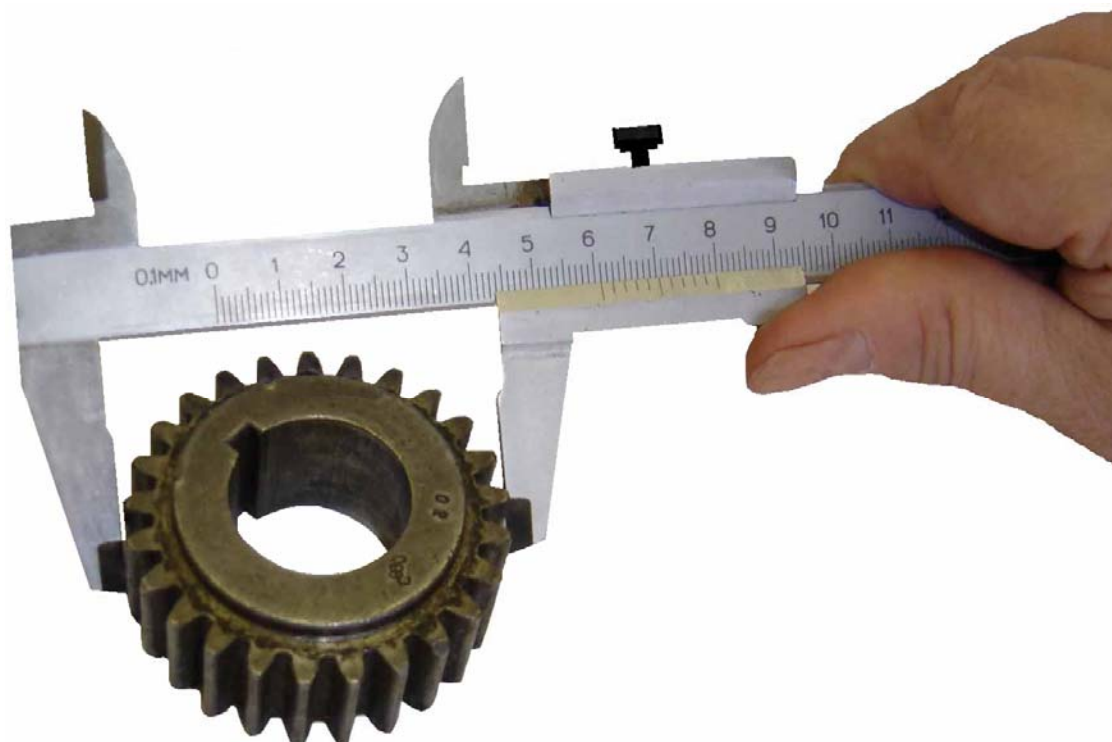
Измерение диаметра вершин зубьев колеса
